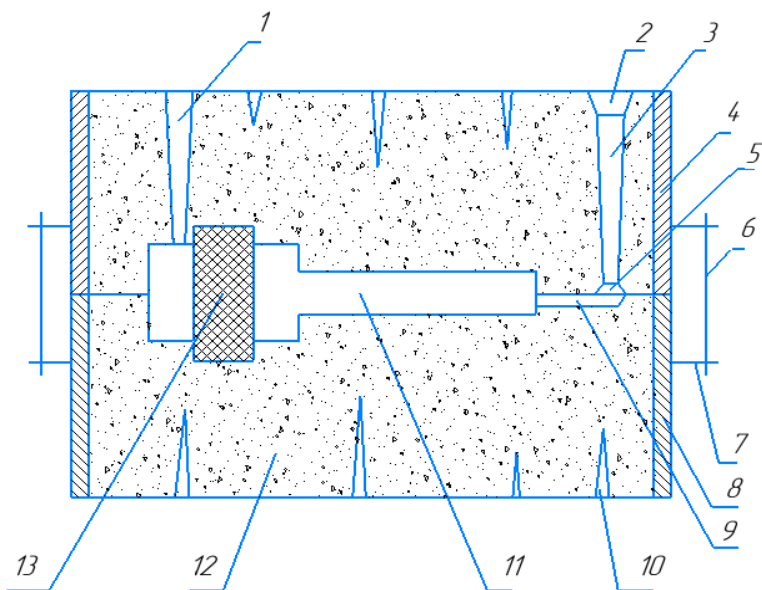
Эскиз литейной формы в сборе для формовки детали «тяга» с вертикальным расположением стержня (вариант разъема модели и формы № 1)
